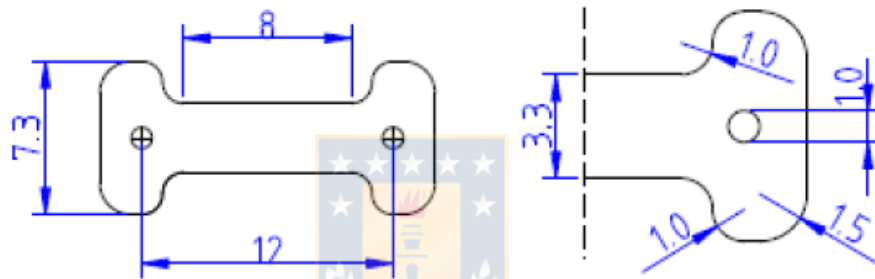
Dimensiones de la probeta fabricada por compactación. Las dimensiones están en mm.
